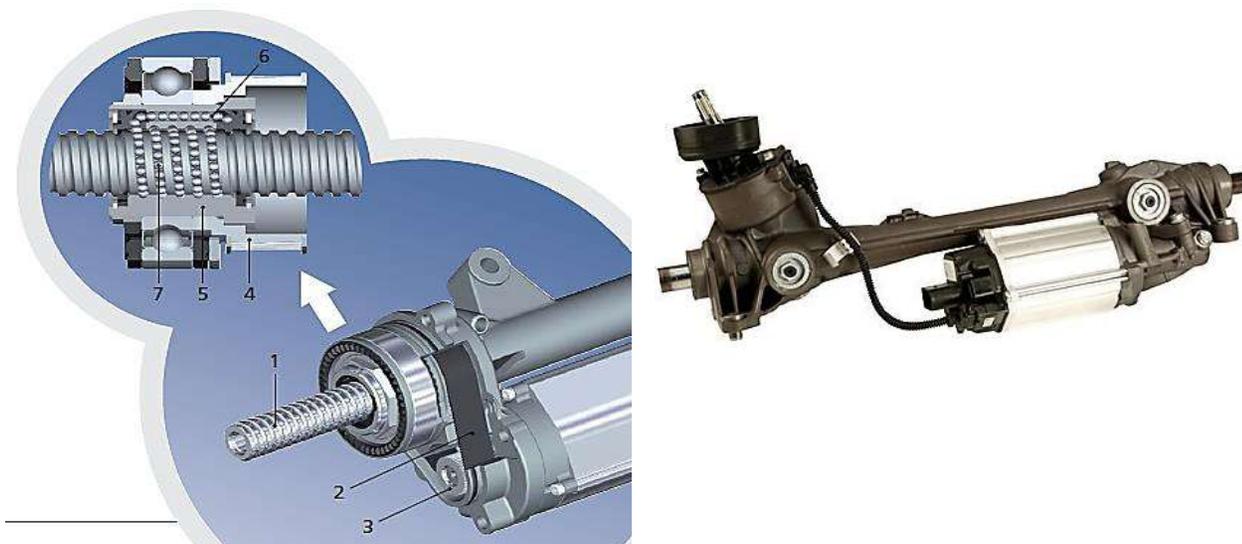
Montaje de motor eléctrico en la cremallera de dirección.
